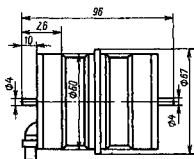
13 Габаритные и установочные размеры двигателя АС-032
